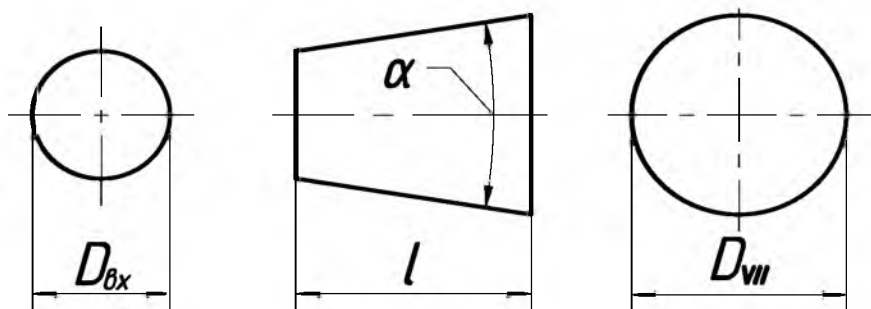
Эскиз перехода к вентилятору ВР-120-45-5
